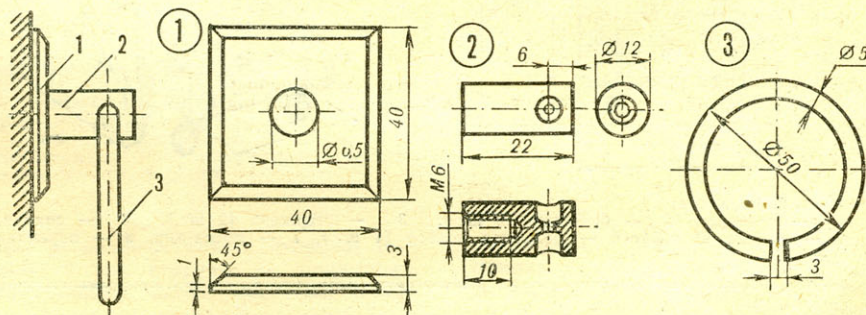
Ручка: 1 — пластина, 2 — гайка, 3 — кольцо.
